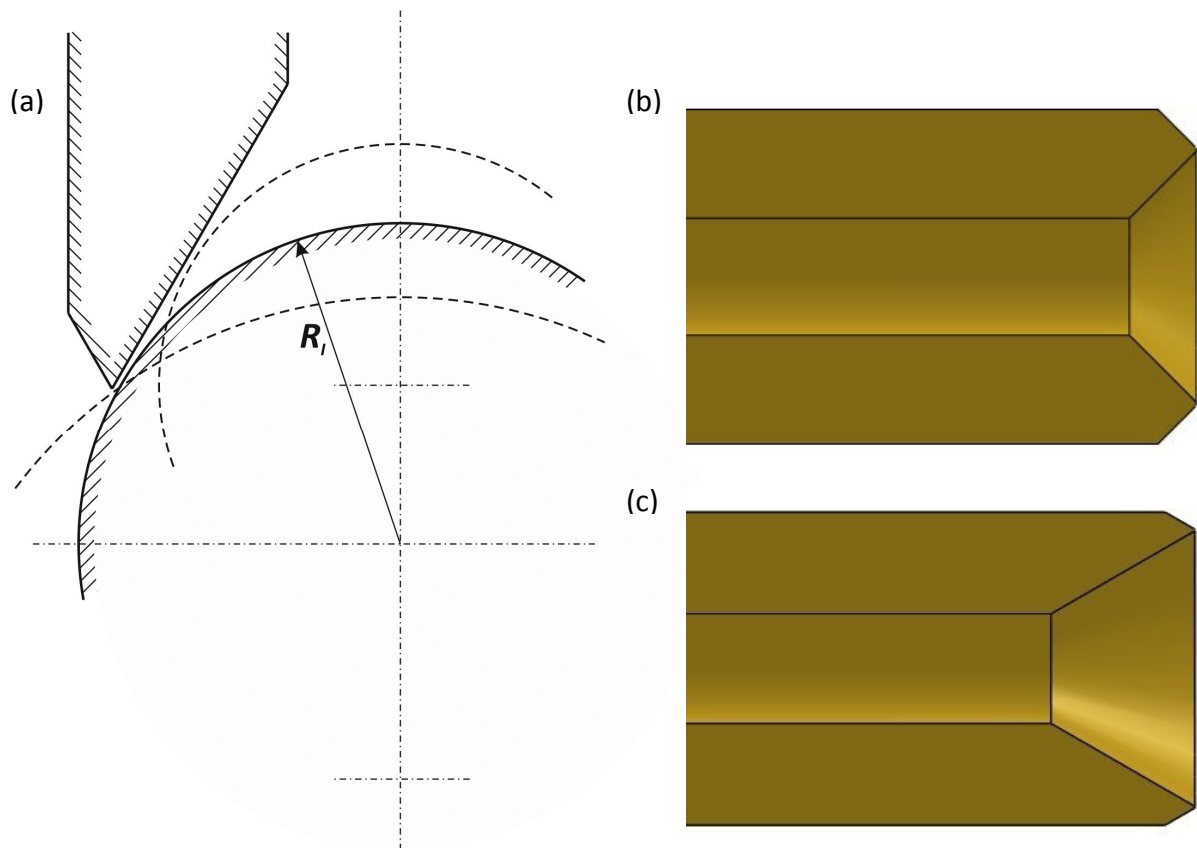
(a) Schematische Darstellung der Innenanfasung mit verschiedenen Kugeldurchmessern; Längsschnitt des Rohres mit (b) 90° Austrittskegel; (c) 60° Austrittskegel
